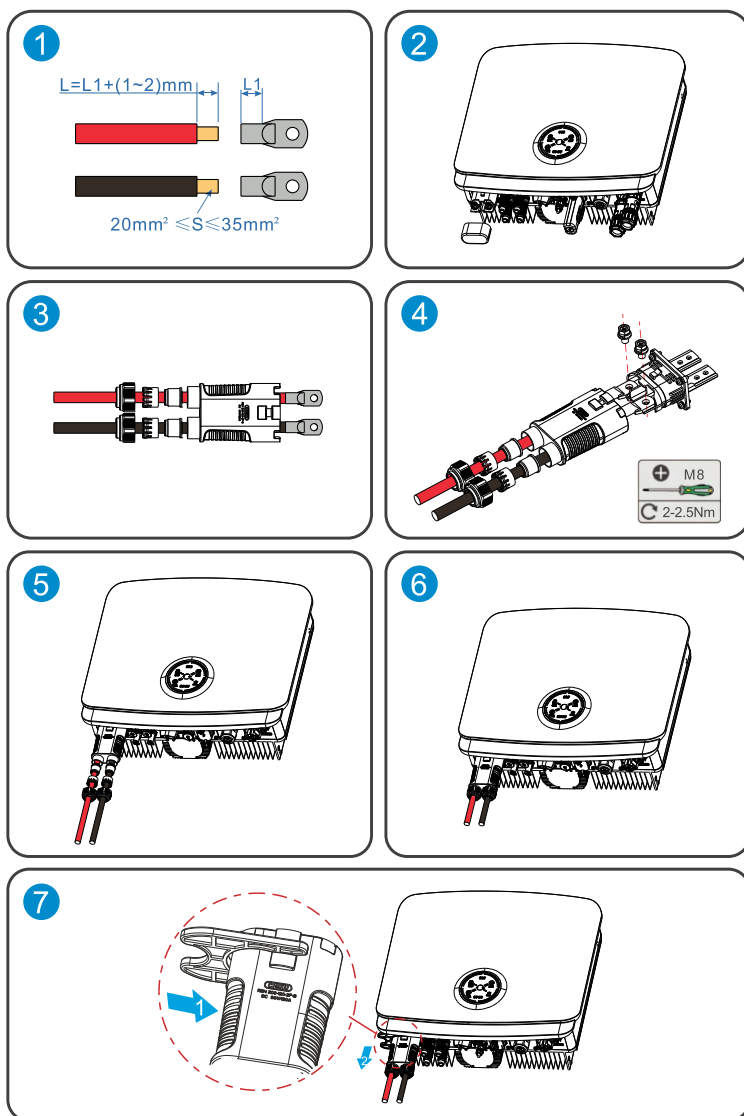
Passaggi per l'installazione e il collegamento del cavo della batteria
